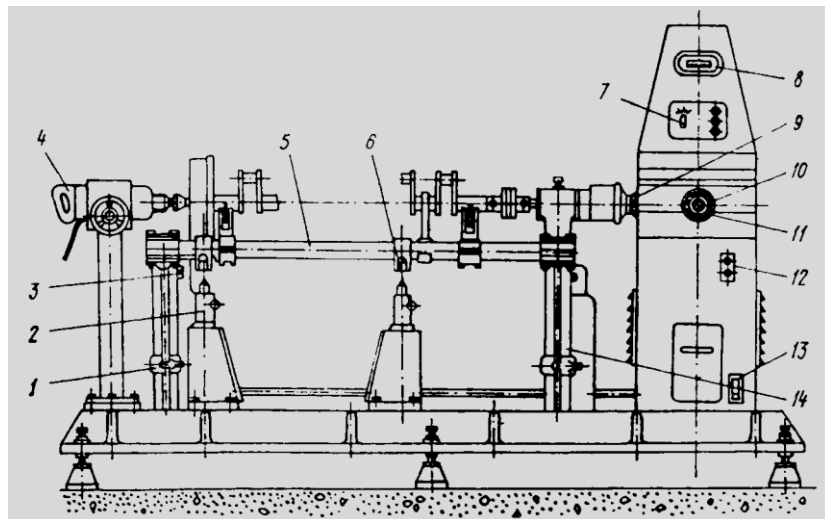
Верстат для динамічного балансування колінчастих валів: 1 – пружина стійки; 2 – стійка; 3 - магнітний датчик; 4 – дріль; 5 – віброрама; 6 – маховик; 7 – перемикач; 8 – гальванометр; 9 – боковий лімб; 10 – лімб рухомий; 11 – лімб нерухомий; 12 – пусковий вмикач; 13 – гальмо; 14 – гасник коливань.
